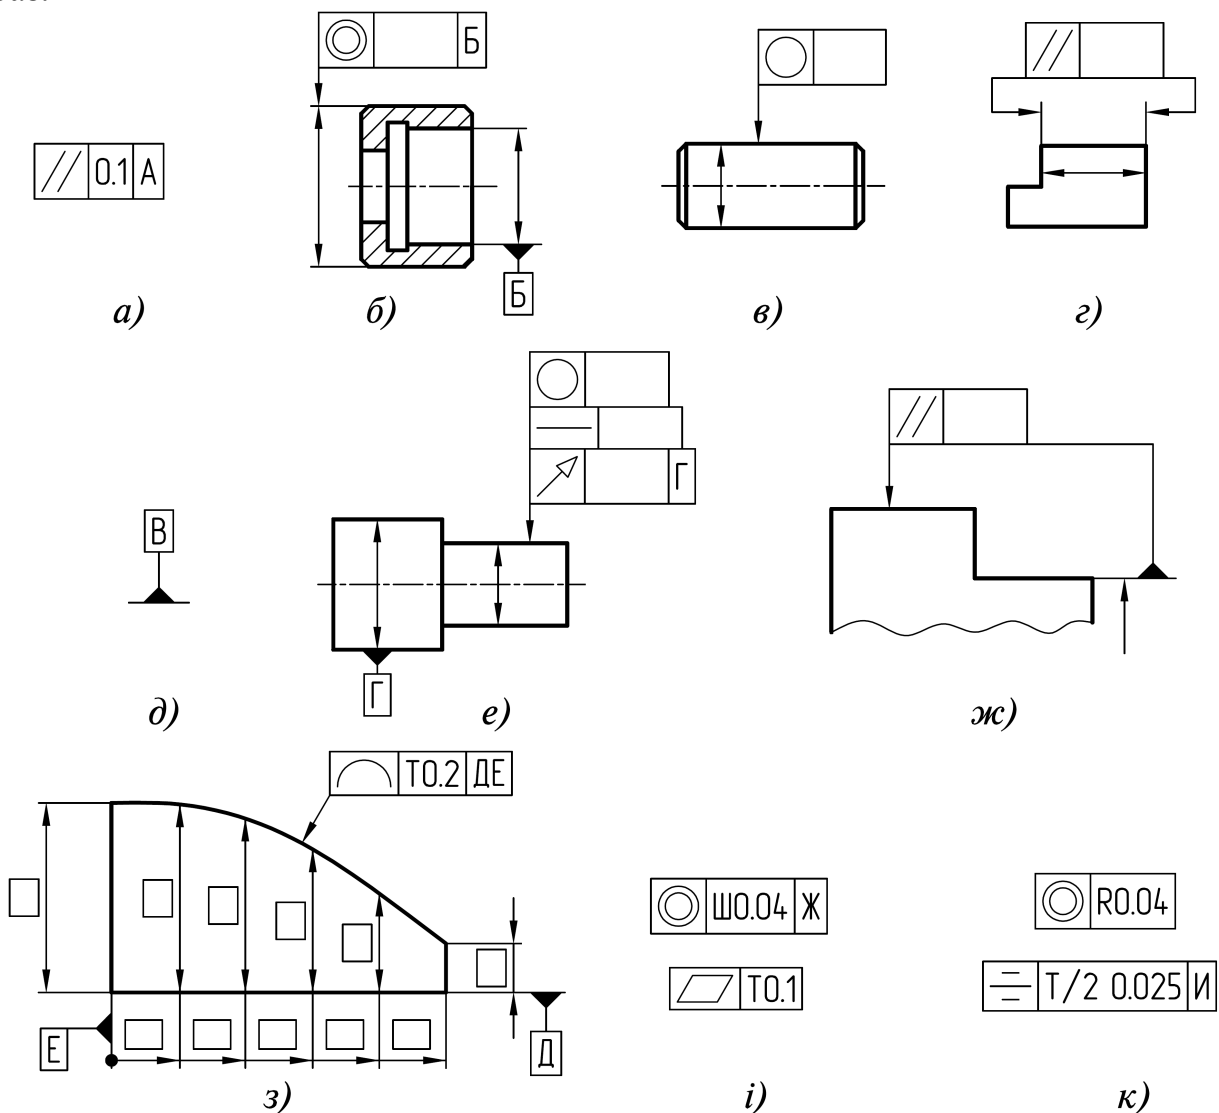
Умовне позначення допусків форми та розташування поверхонь
